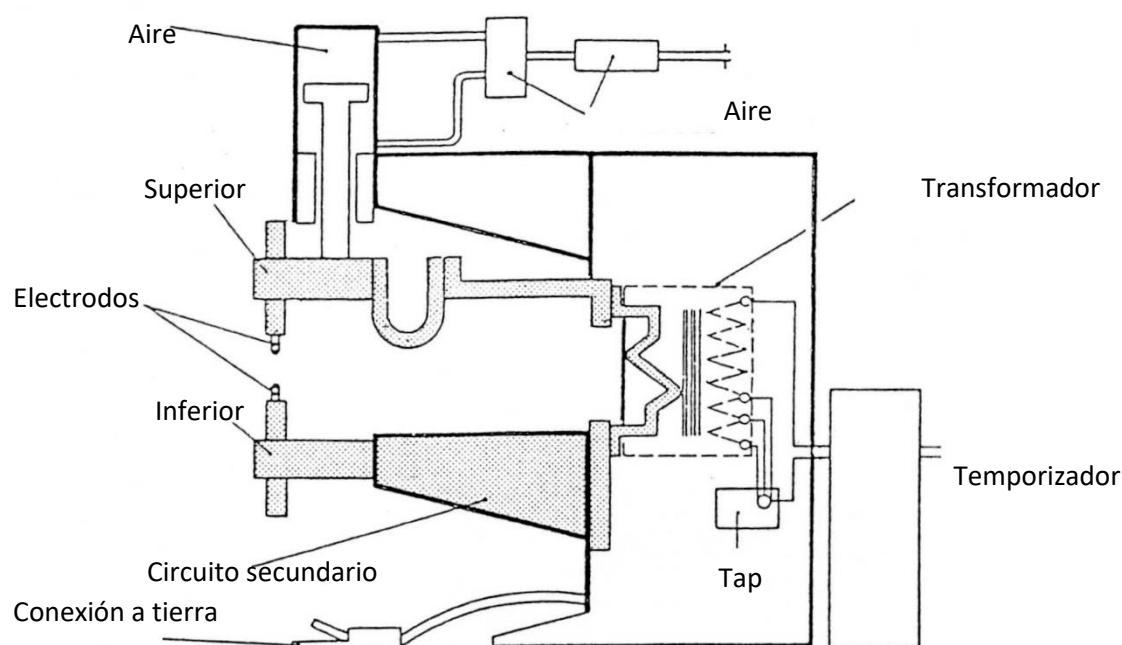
Máquina de soldadura por puntos de pedestal. Fuente: TWI
